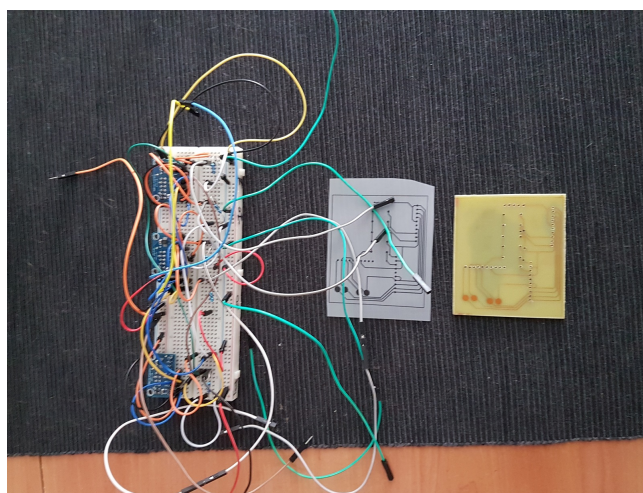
Comparación del conexionado en protoboard con el diseño de la PCB.
